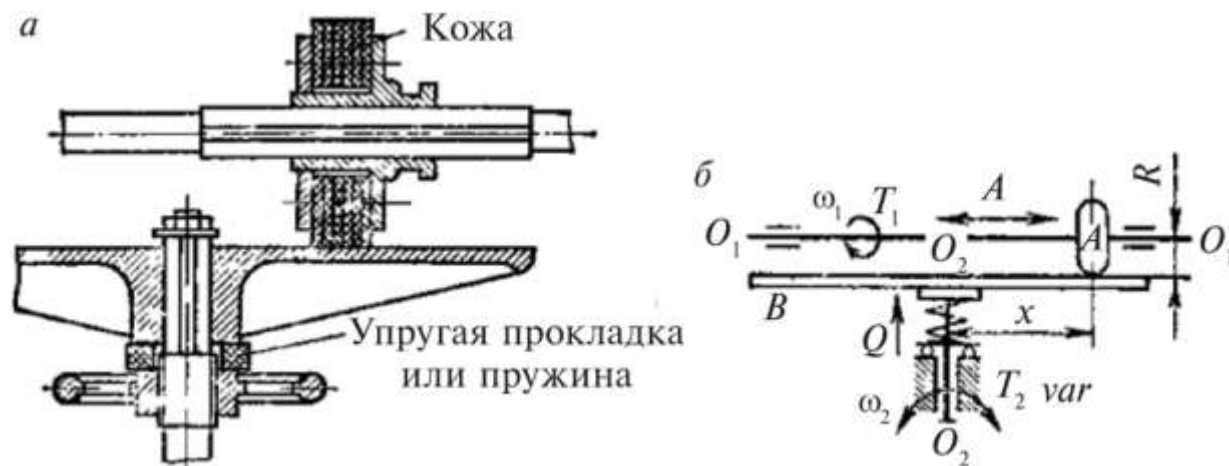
Лобовой вариатор (а), схема лобового вариатора (б)
